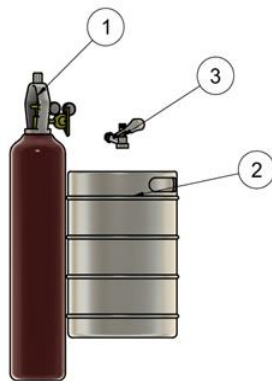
Vista explodida dos principais componentes periféricos da máquina de arrefecimento de cerveja
